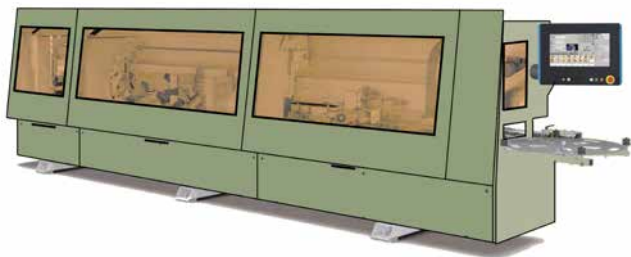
Beispiel einer gekapselten Holzbearbeitungsmaschine
